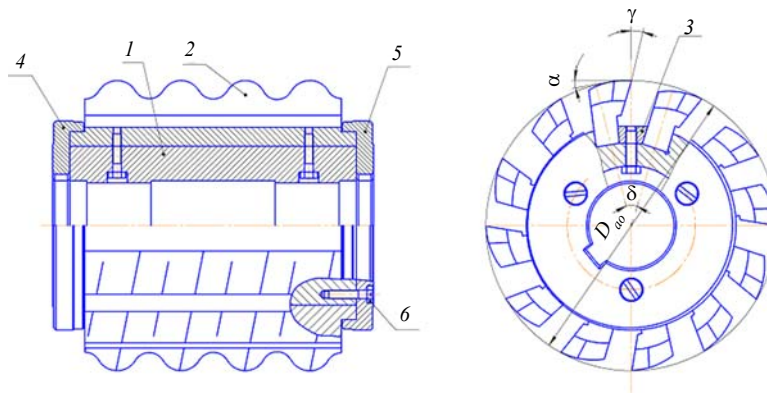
Сборная фасонная червячная фреза с поворотными рейками
